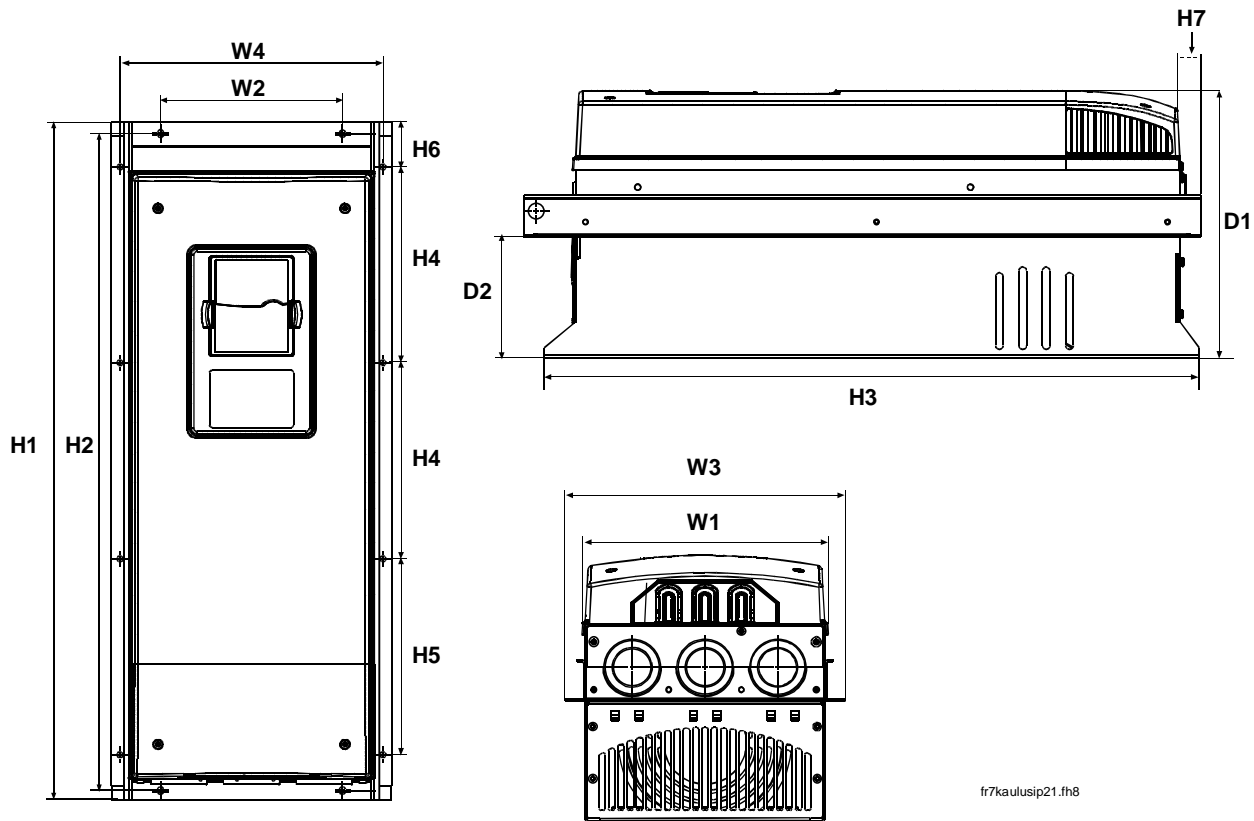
Dimensões Vacon NX_, FR7 e FR8, montagem por flange
